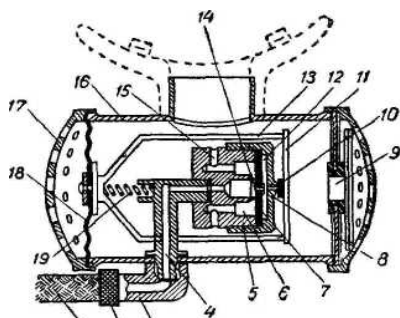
Легочный автомат конструкции И. Балдина: 1 - шланг; 2 - накидная гайка; 3 - угловой штуцер; 4 - стойка; 5 - клапанная обойма; 6 - воздушная полость; 7 - мембрана; 8 - накидная гайка; 9 - клапан выдоха; 10 - воздушный клапан; 11 - пластина; 12 - затворная полость; 13 - серьга; 14 - втулка; 15 - воздушный канал; 16 - корпус автомата; 17 - крышка; 18 - мембрана; 19 - пружина
